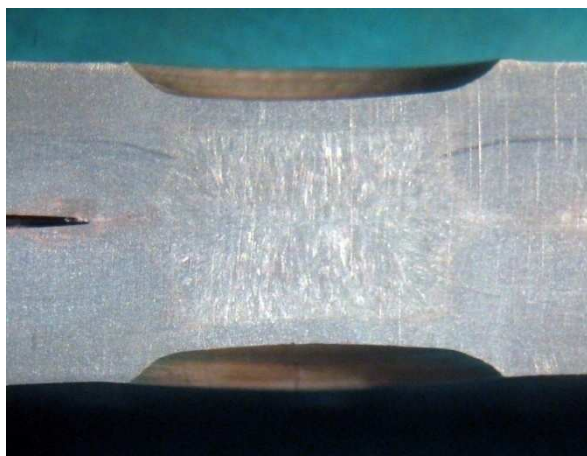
30. Macrografía del punto de soldadura en la probeta de 3.0 mm (10x)
